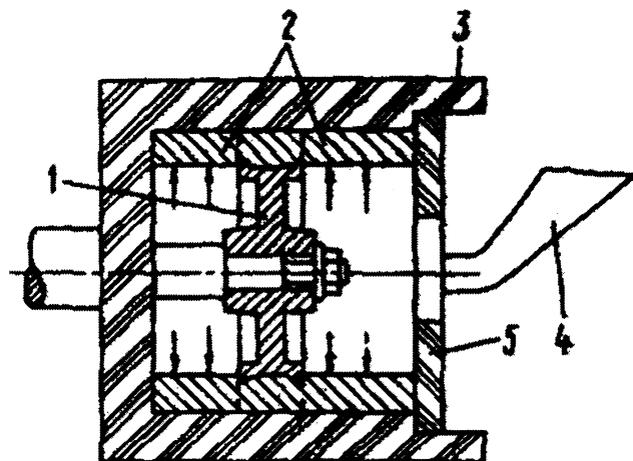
Схема центробежной заливки зубчатого колеса: 1 — ступица; 2 — заливаемый сплав; 3 — вращающаяся изложница; 4 — заливочный лоток; 5 — крышка
